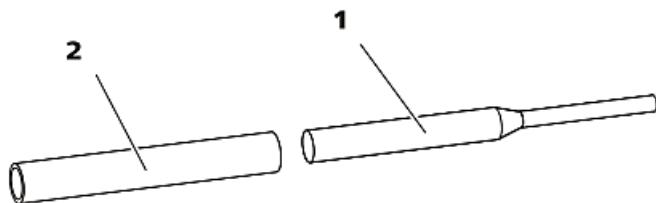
Приспособление для установки уплотнения поршня (6.2617.010)
